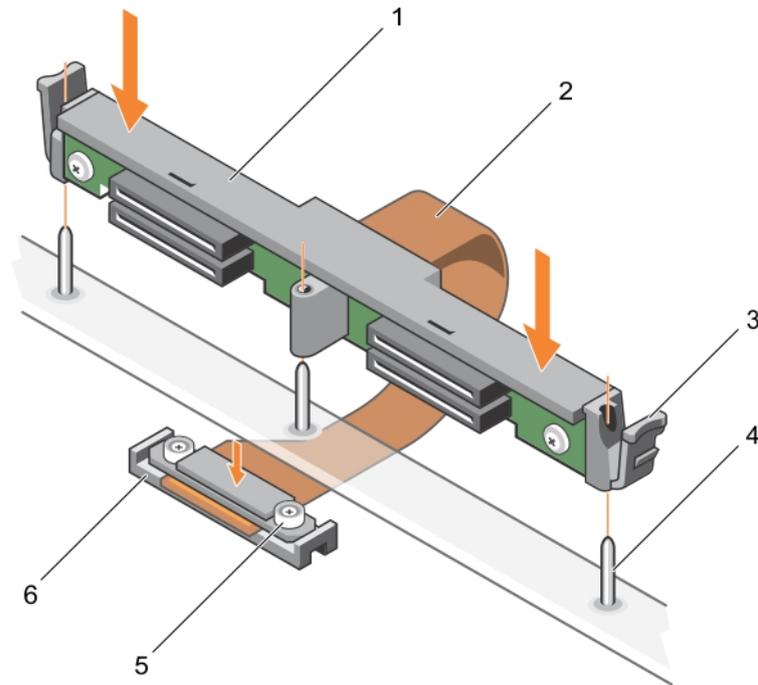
Installation du fond de panier de SSD de 1,8 pouce (x4)
